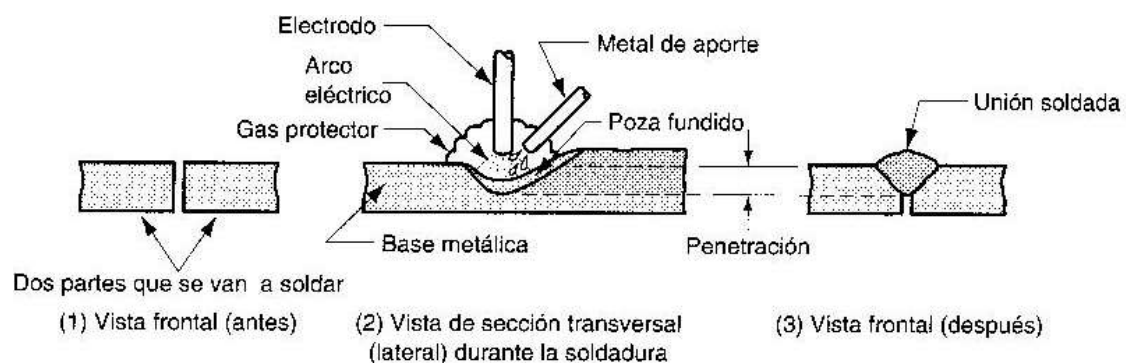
Descripción proceso de soldadura SMAW.
